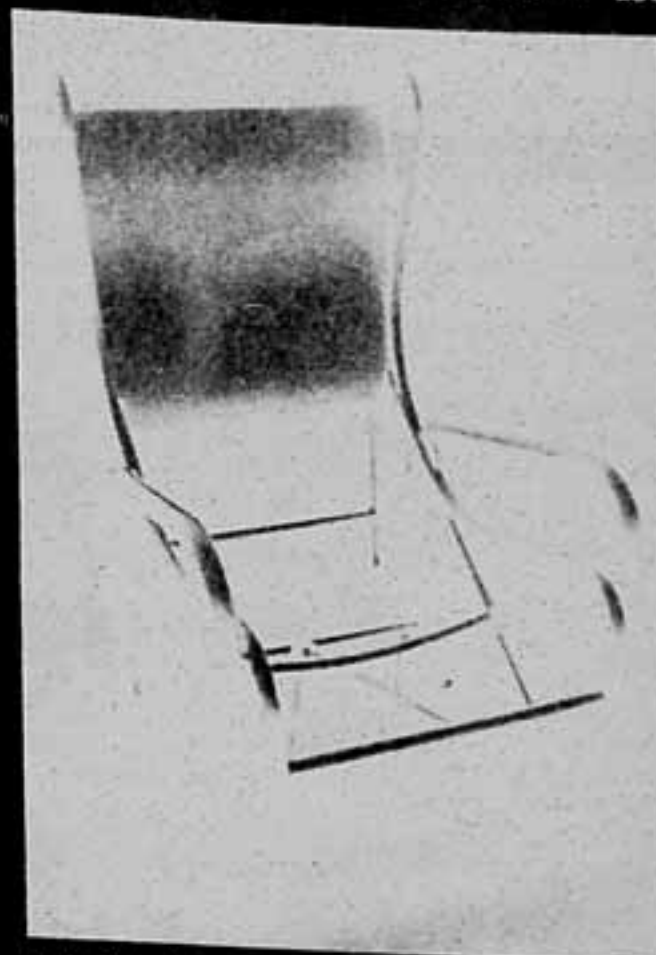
Kabinensessel für ein Verkehrsflugzeug in Elektronmetallrohren geschweißt.
